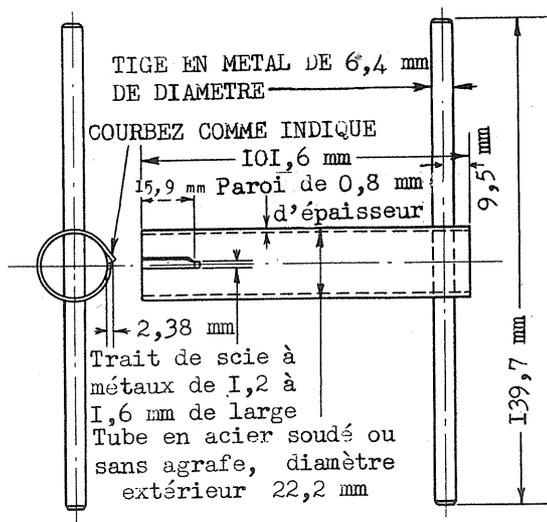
OUTIL SUGGÈRE POUR MONTER LE RESSORT D'EN-
